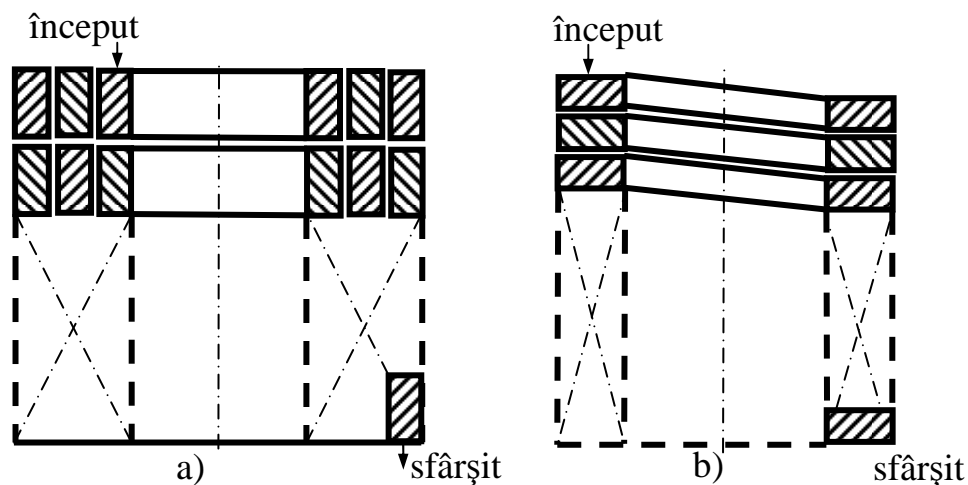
Secțiune longitudinală prin bobine cilindrice înfășurate pe muchie, din bare de cupru având secțiunea transversală: a – dreptunghiulară; b – trapezoidală.
